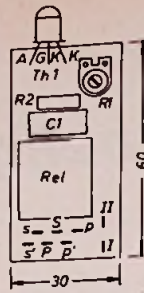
Constructieschets van het montageplaatje, op halve grootte van de schakeling van fig. 1.
